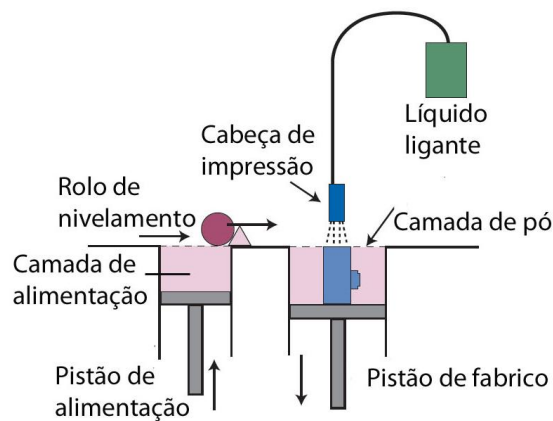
Esquema de um equipamento de impressão 3D. Adaptado de [86]
